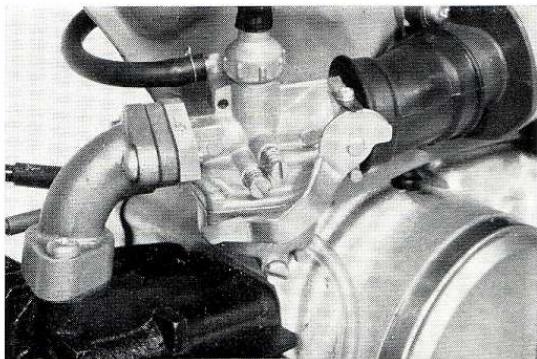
RÉGLAGE DU CARBURATEUR EN MARCHE A VIDE.
